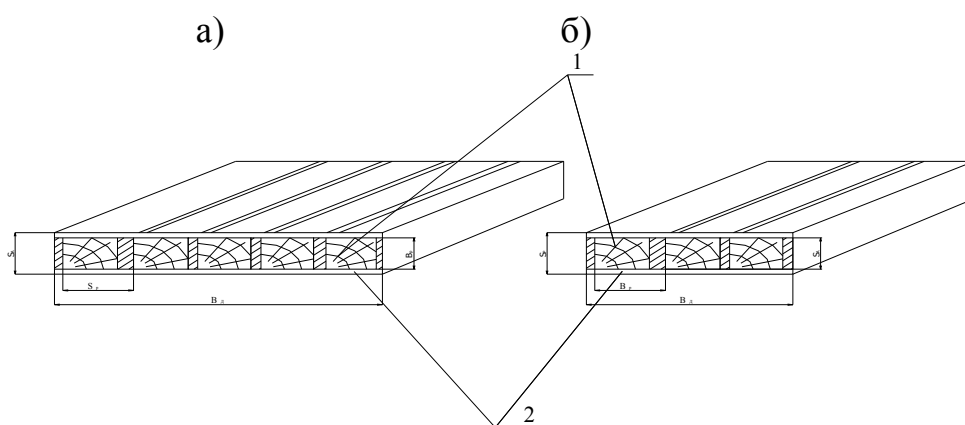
Схема раскроя досок на черновые заготовки (рейки):
